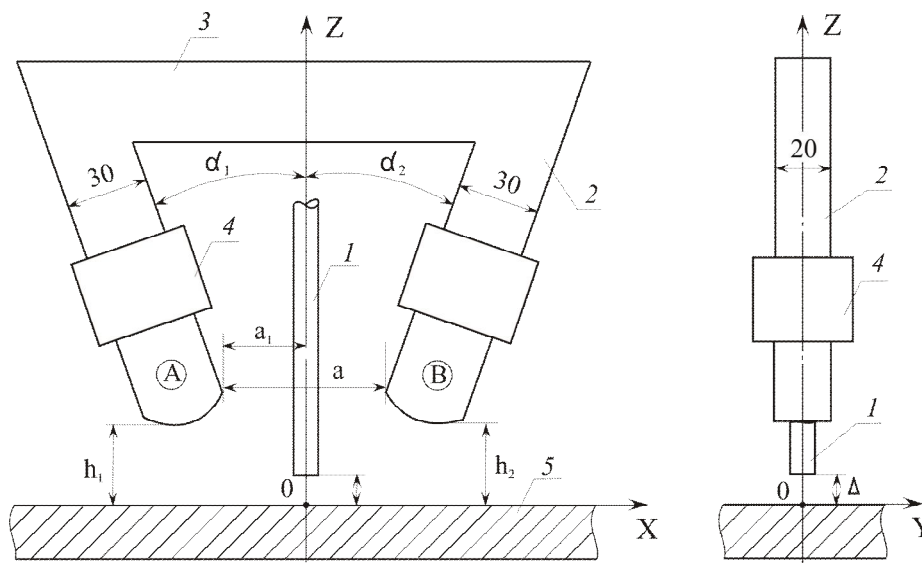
Схема конструкции УВ ПОМП: 1 – электродная проволока; 2 – стержни; 3 – перемычка; 4 – катушки; 5 – изделие (пластина)
